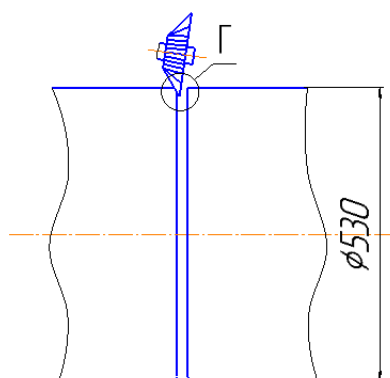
Новая технология подготовки стыков к сварке
